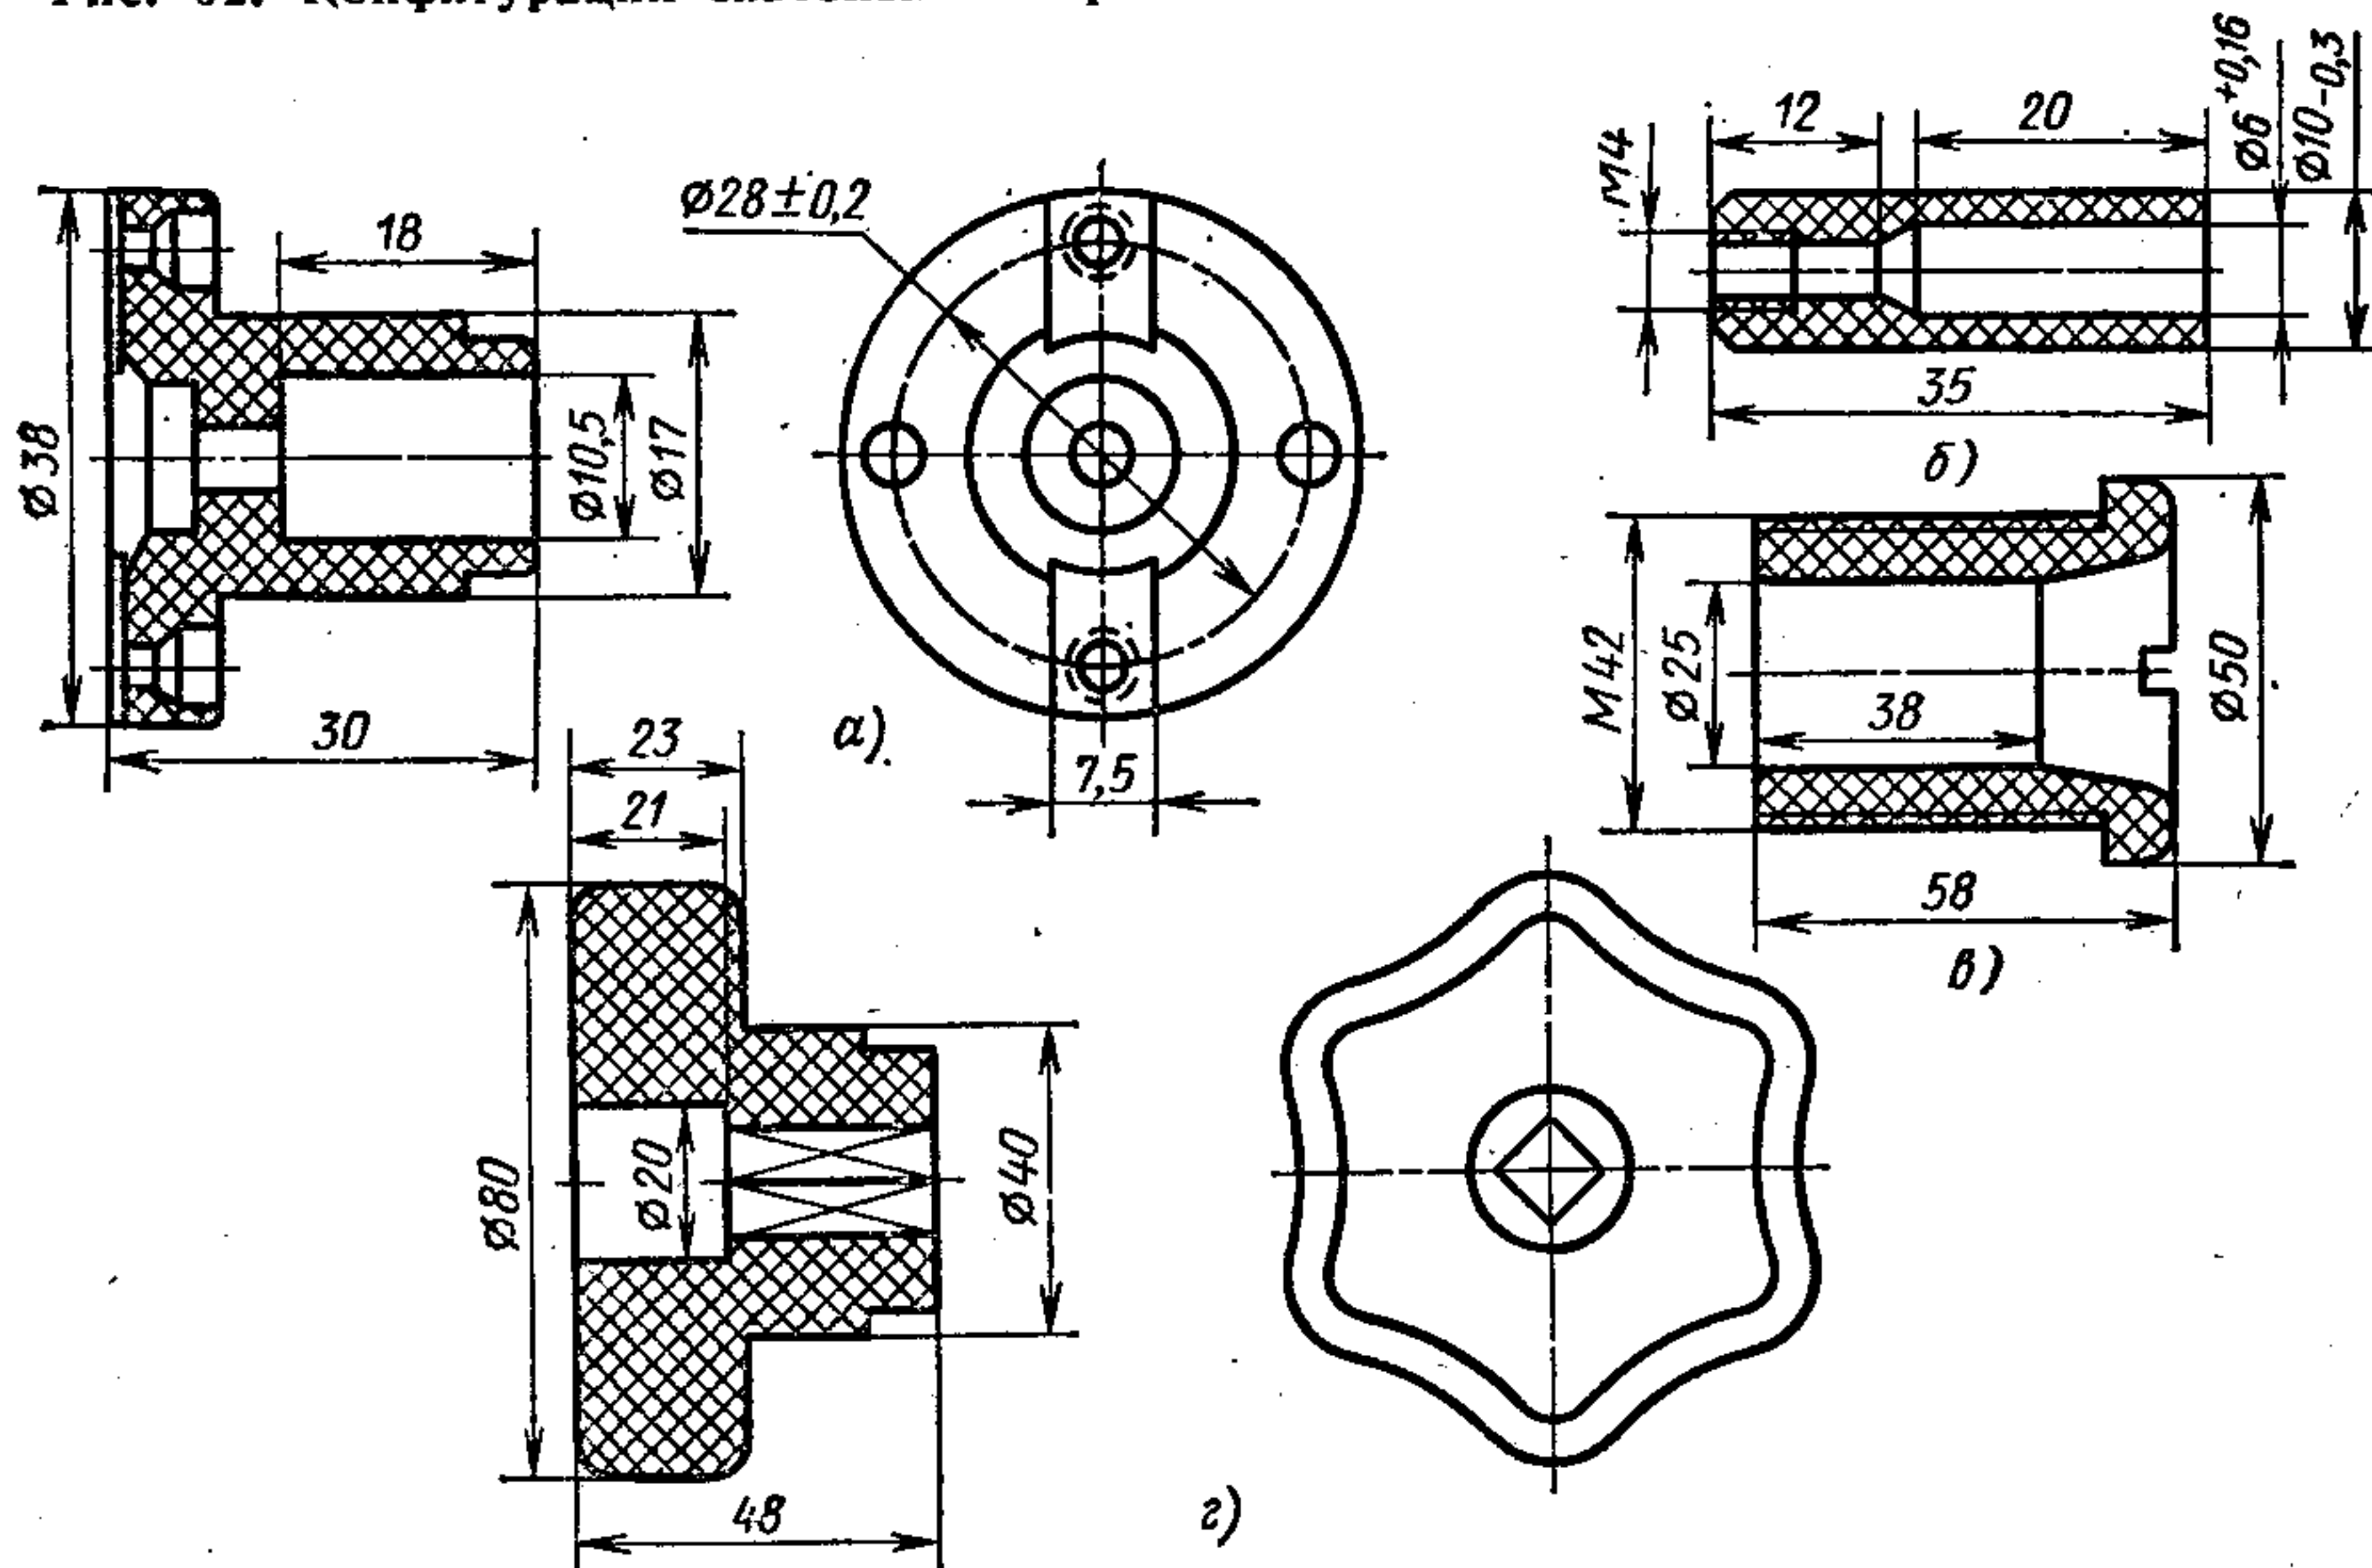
Типовые детали с отверстиями: а, б — корпуса (пресс-материал Э2-330-02); в — втулка (капрон); г — рукоятка (пресс-материал Э2-330-02)
